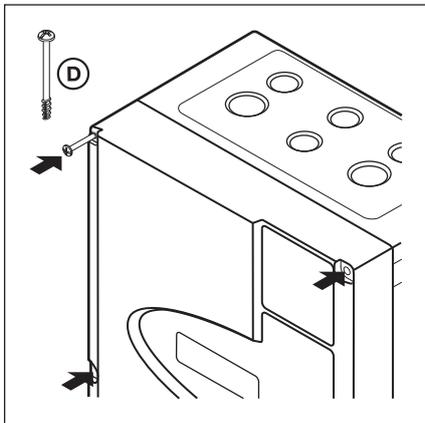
Alle Deckelschrauben (6x) montieren
